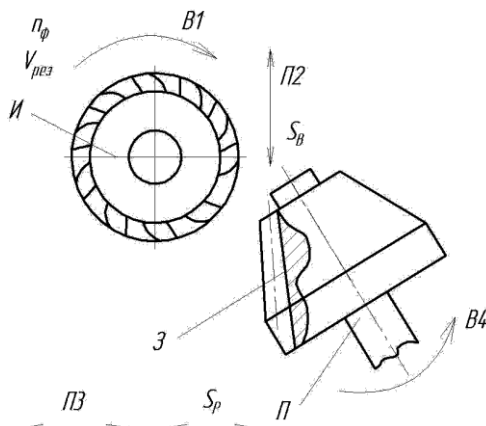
Рабочая зона зубофрезерного станка-полуавтомата:
